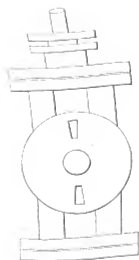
Seitenansicht der Ventilschleife am Dampfzylinder
